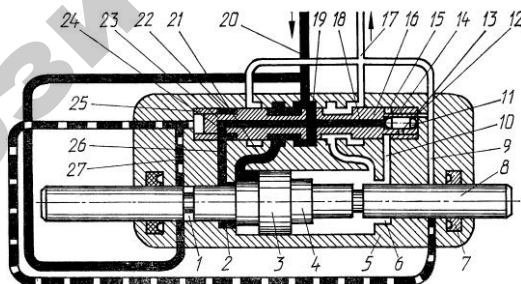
Гидродвигатель возвратно-поступательного движения:
